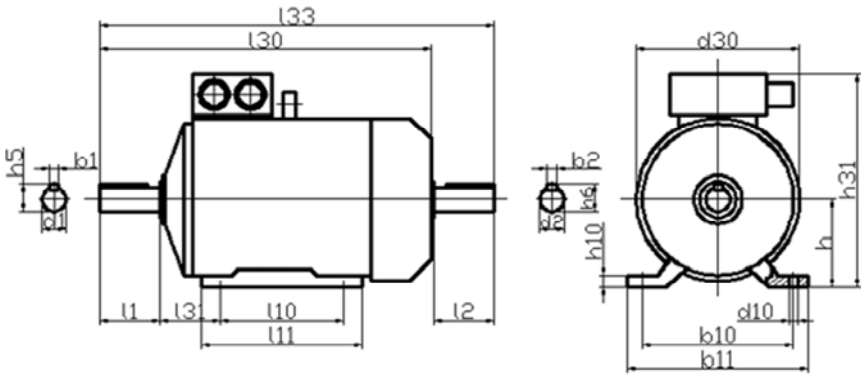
Габаритный чертеж электродвигателя серий АИР, А, 4А, 5А, АД на лапах с двумя цилиндрическими концами вала любого пространственного положения (исполнение по способу монтажа IM1082)
